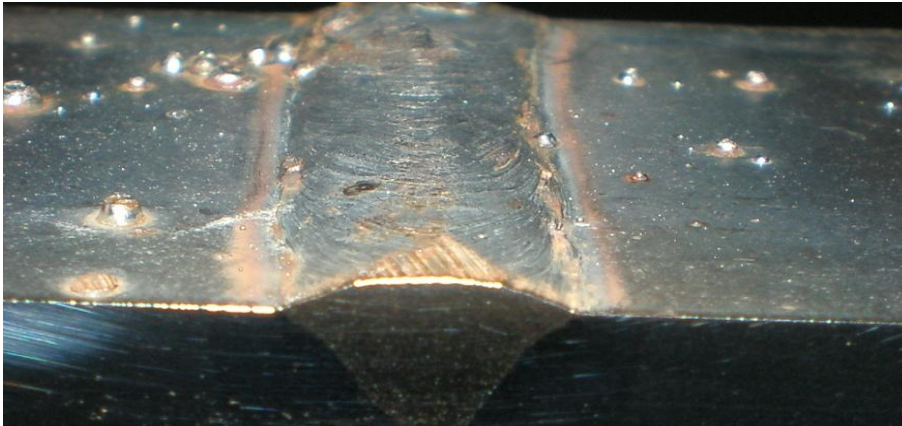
Probeta Acero AISI 1010 soldada bajo la condición de 132 Amp.
